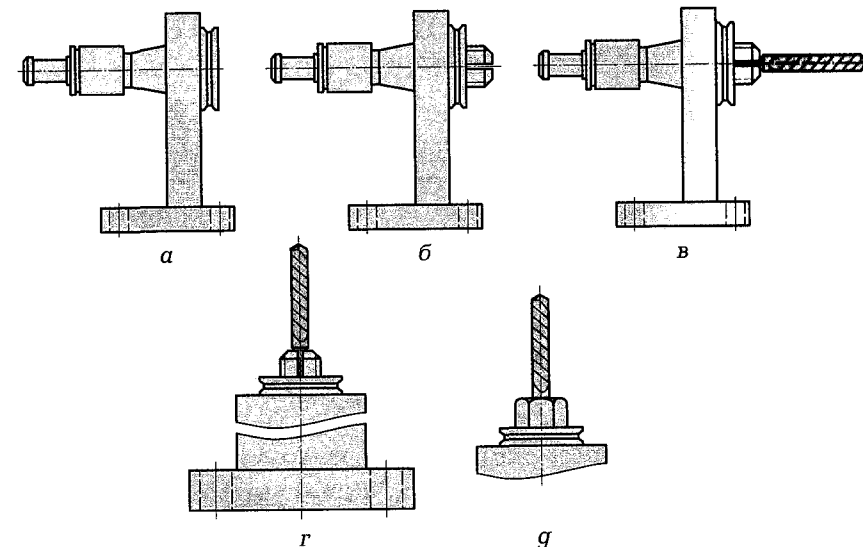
Последовательность сборки оправки с осевым инструментом (сверлом):
